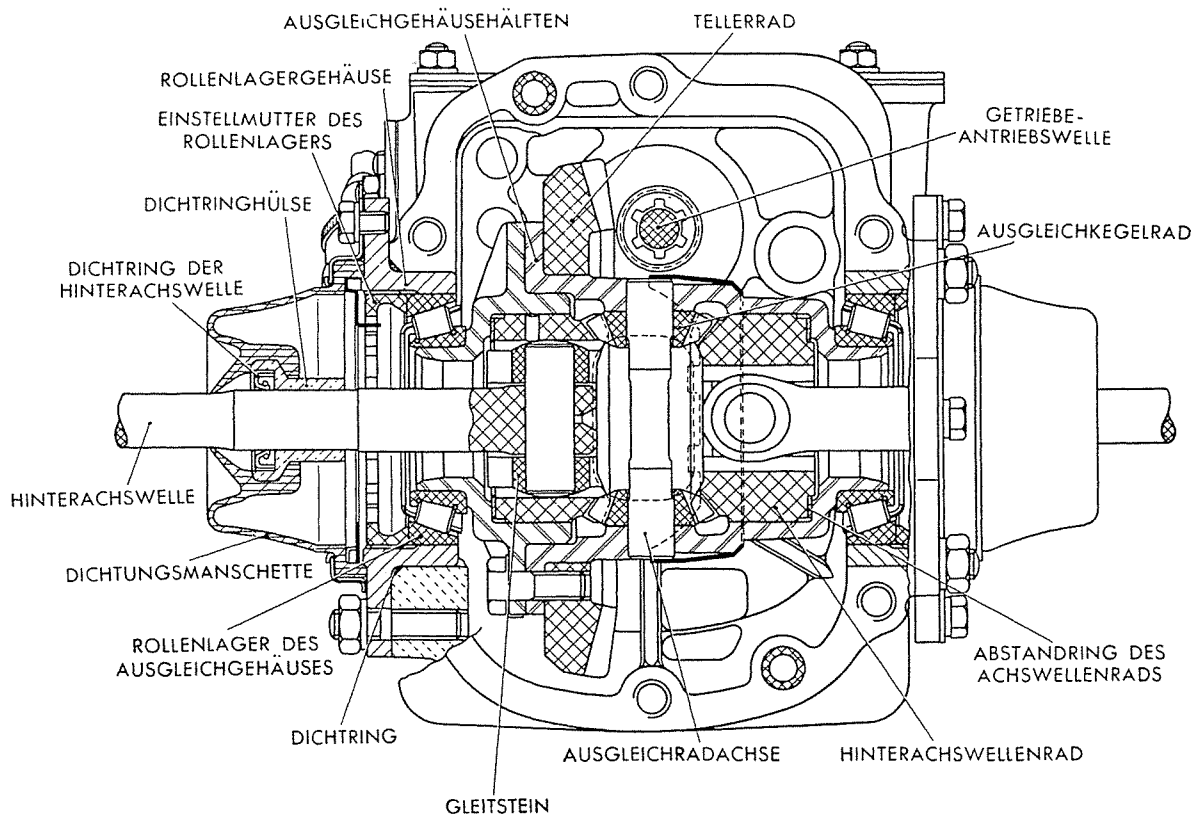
Querschnitt des Wechsel- und Ausgleichgetriebes durch die Hinterachswellen.
